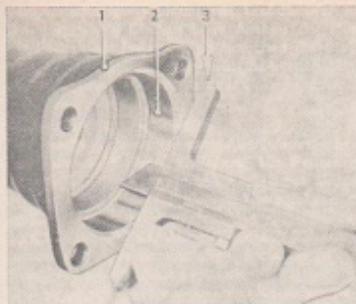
Tiefe des Sitzes für Hinterschwellenkugellager messen
